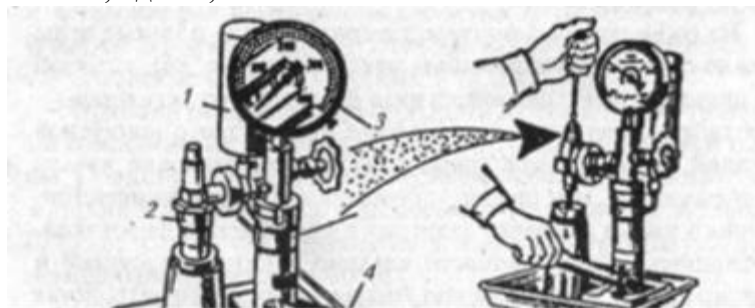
Прибор КП-1609А для проверки и регулировки форсунок
